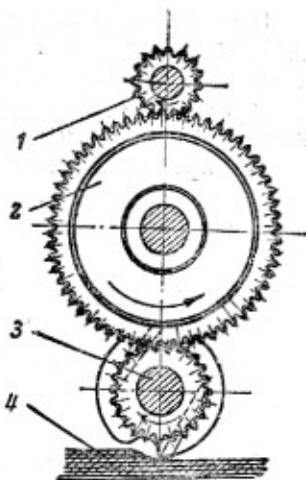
Схема редуктора рубанка ЭРБ-100:
